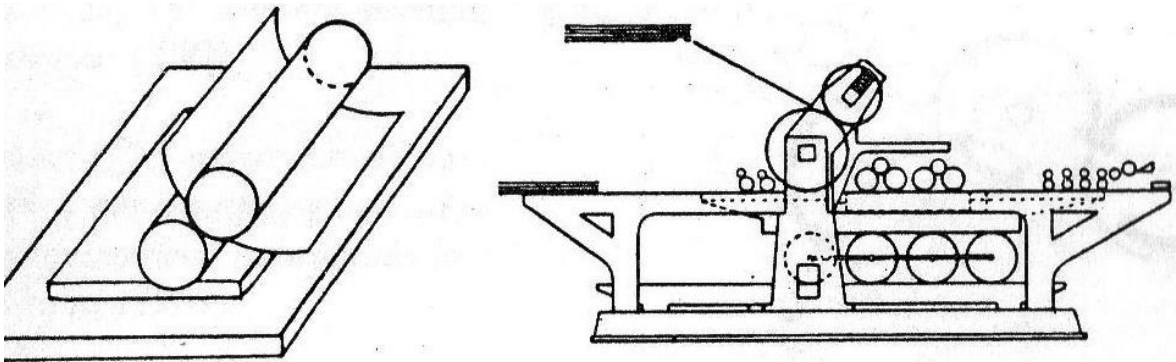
Máquina de impresión indirecta plano-cilíndrica (der.) y su principio de impresión (izq.).
